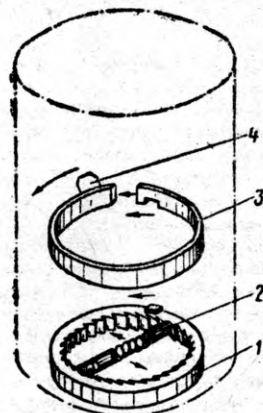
Механизм вращающего поршня: 1 — зубчатое кольцо внутри поршня; 2 — маятниковый механизм с двойной собачкой; 3 — демпфирующее устройство; 4 — устройство для соединения с поршнем.
